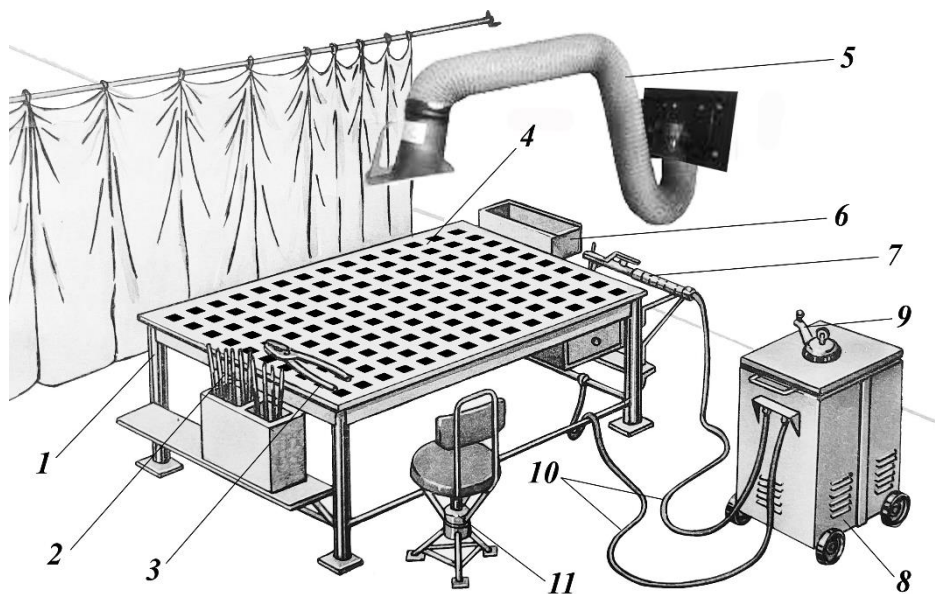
Стаціонарний зварювальний пост ручного дугового зварювання:
